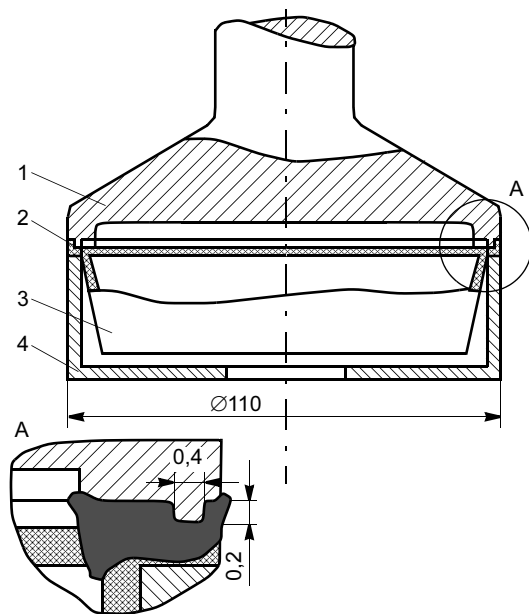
Опора с изделием: 1 — волновод; 2 — крышка; 3 — коробка; 4 — опора
